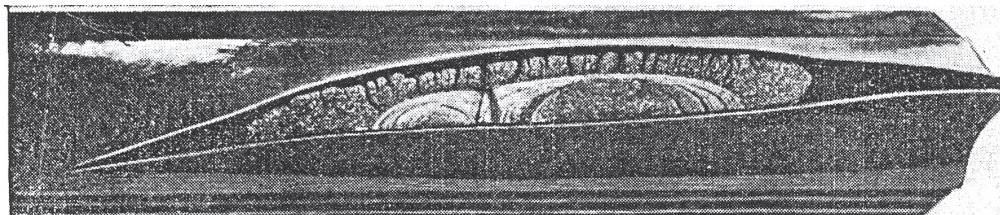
Поверхность усталостного излома лопатки компрессора
